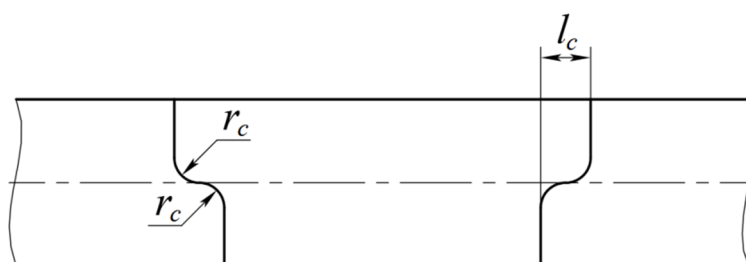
Схема безотходного раскроя трубы на заготовки
